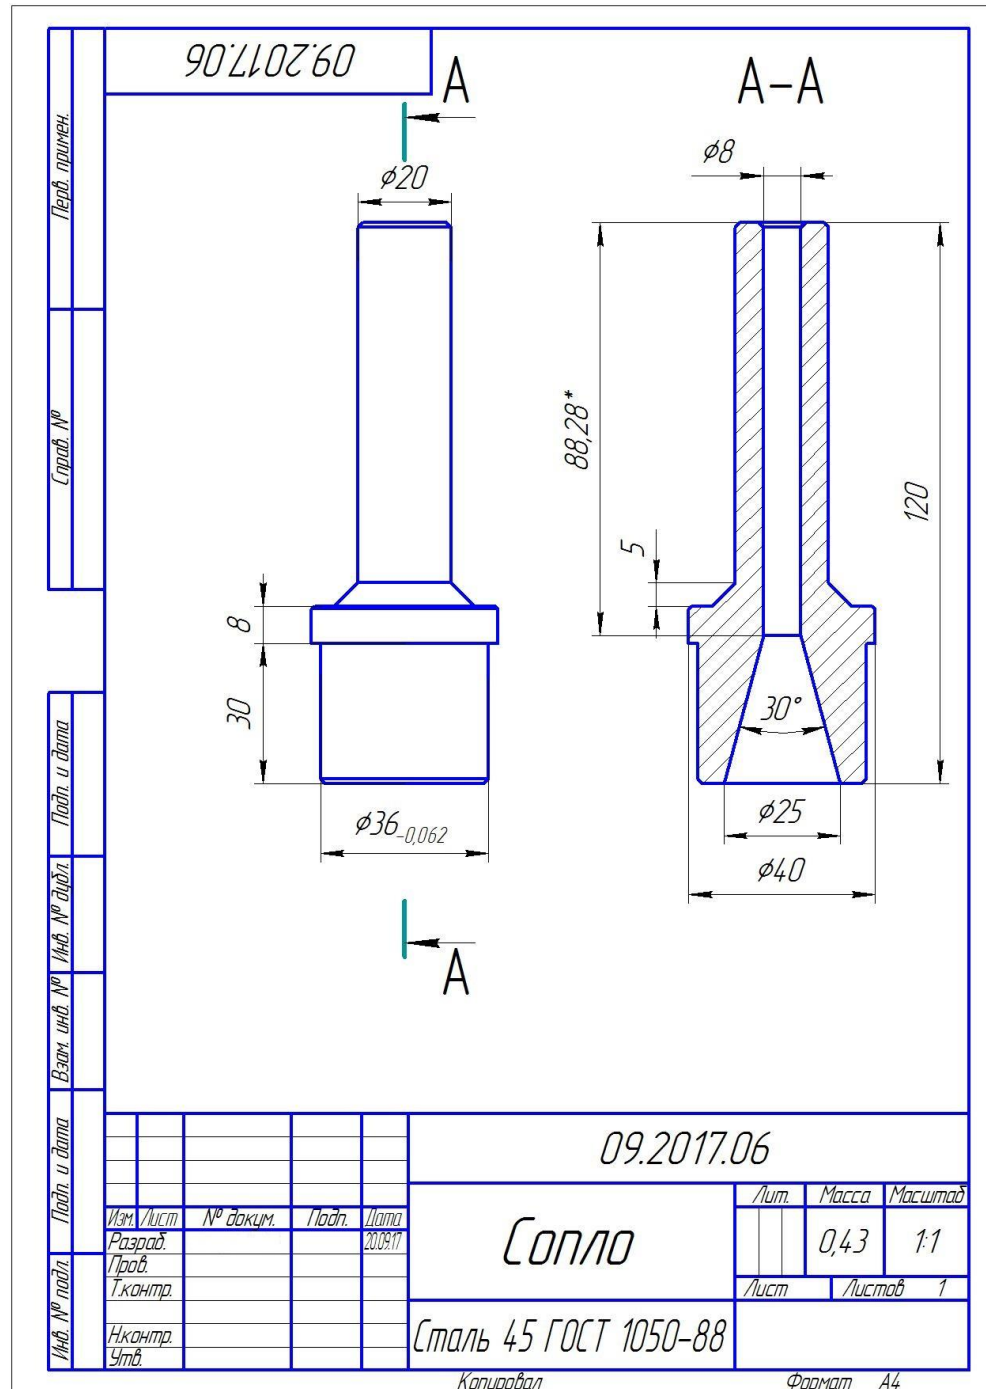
Чертеж сопла для установки пескоструйной обработки
